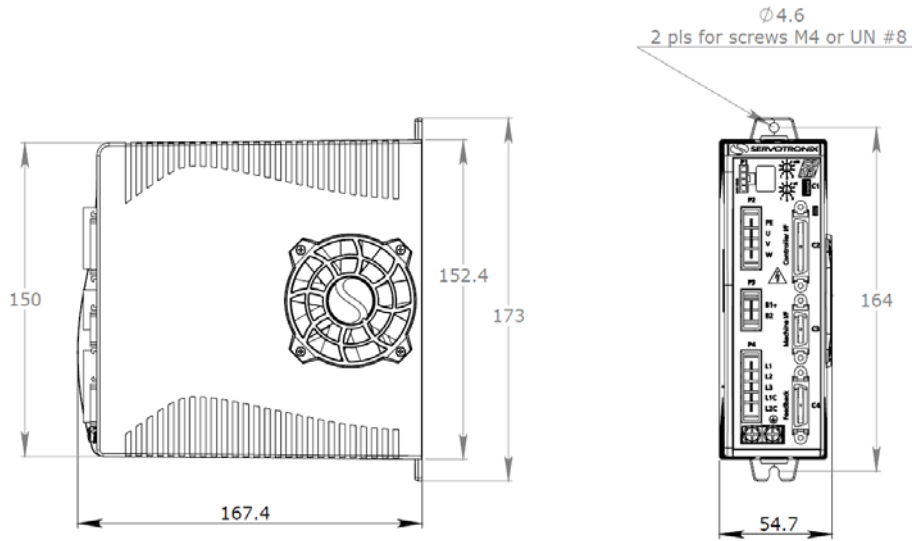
中压 CDHD-4D5/CDHD-006 - 120/240 VAC - 外形尺寸 (mm)
